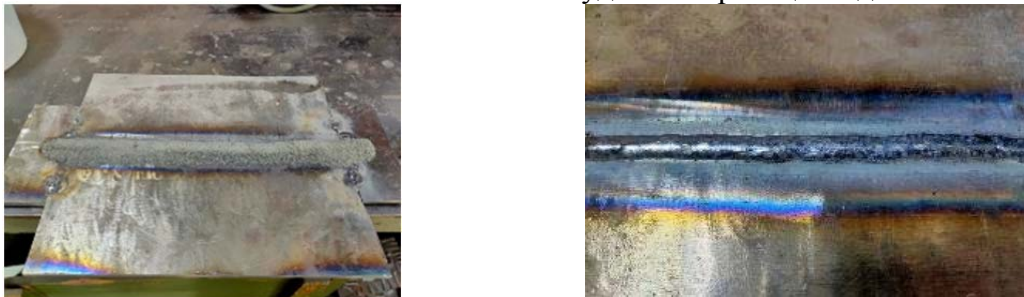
Внешний вид сварного соединения при сварке под слоем экспериментального флюса
